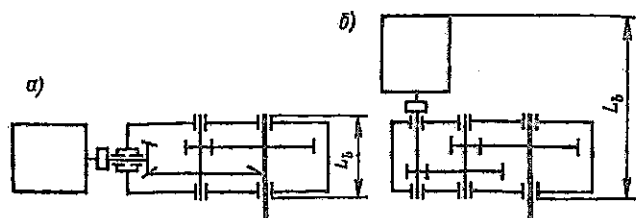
Компоновочные схемы передач: а — коническо-цилиндрическая; б — цилиндрическая
